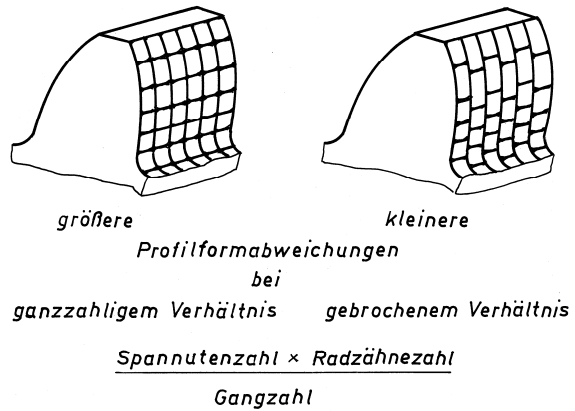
/13 Profil-Formabweichungen der Flankenfläche beim mehrgängigen Wälzfräsen
